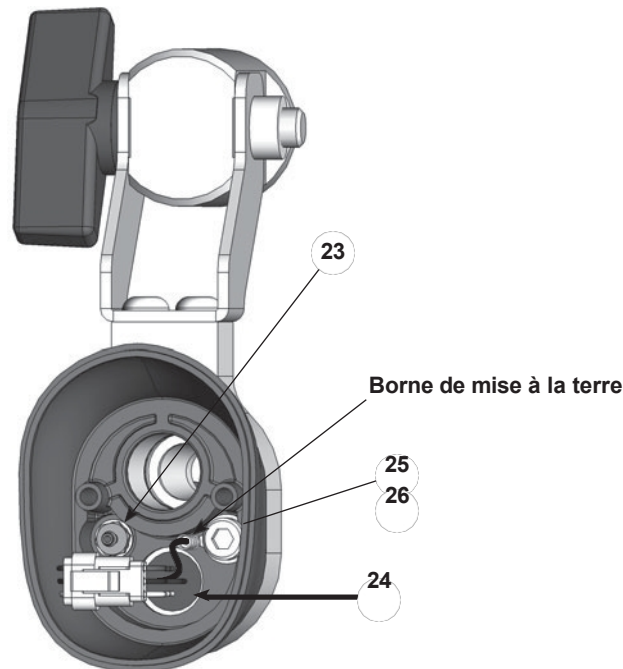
Démontage de l' du pistolet - Remplacement du réceptacle de câble et du raccord cannelé
